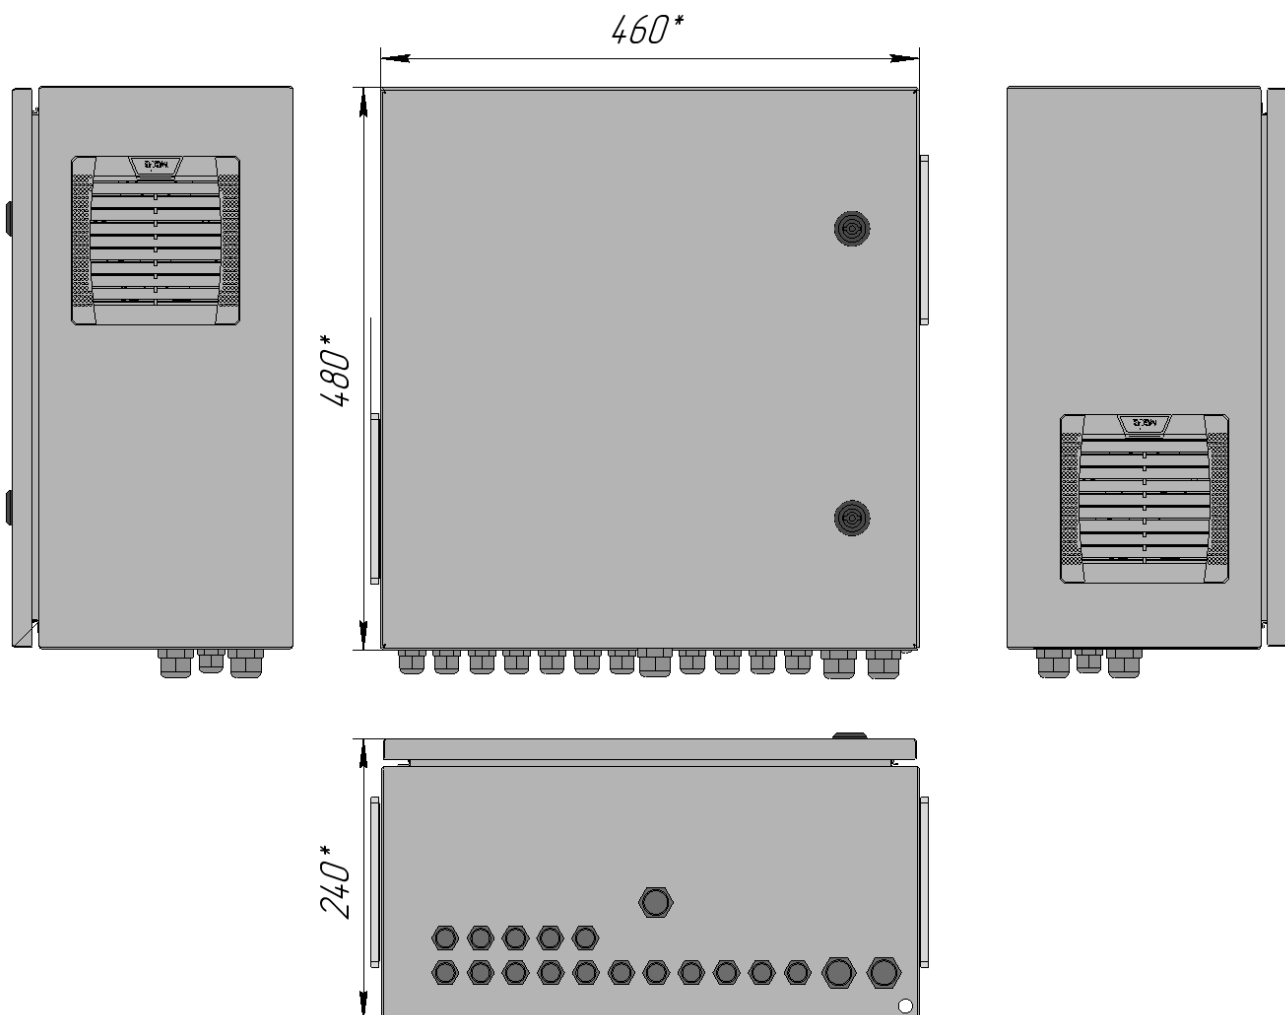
Внешний вид и габаритные размеры Узла доступа 1158S3-F
